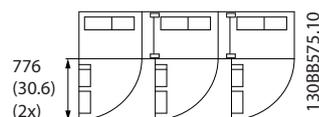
Пространство перед корпусом IP21/IP54, типоразмер F14
